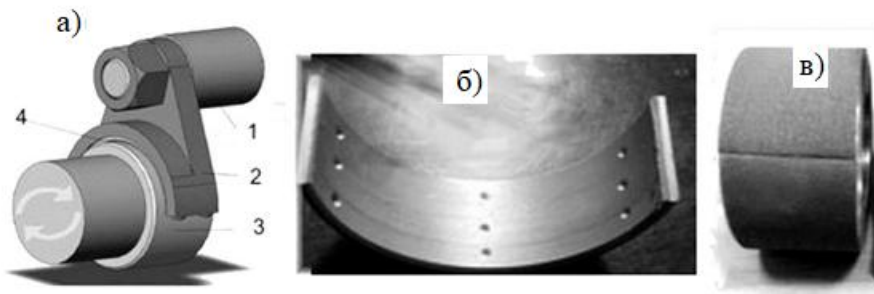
Модель пары трения (а): 1–нажимное устройство, 2 – корпус, 3–вал, 4–вкладыш; б) вкладыш с лунками; в) вал с наклеенной абразивной шкуркой
